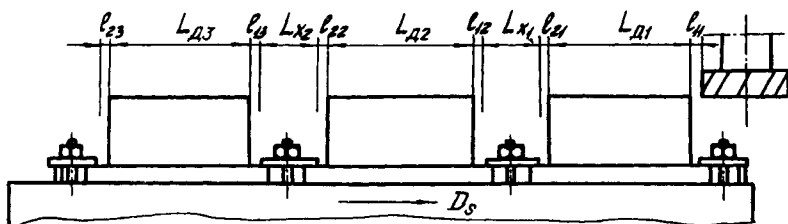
Последовательная многоместная обработка заготовок на фрезерном станке
